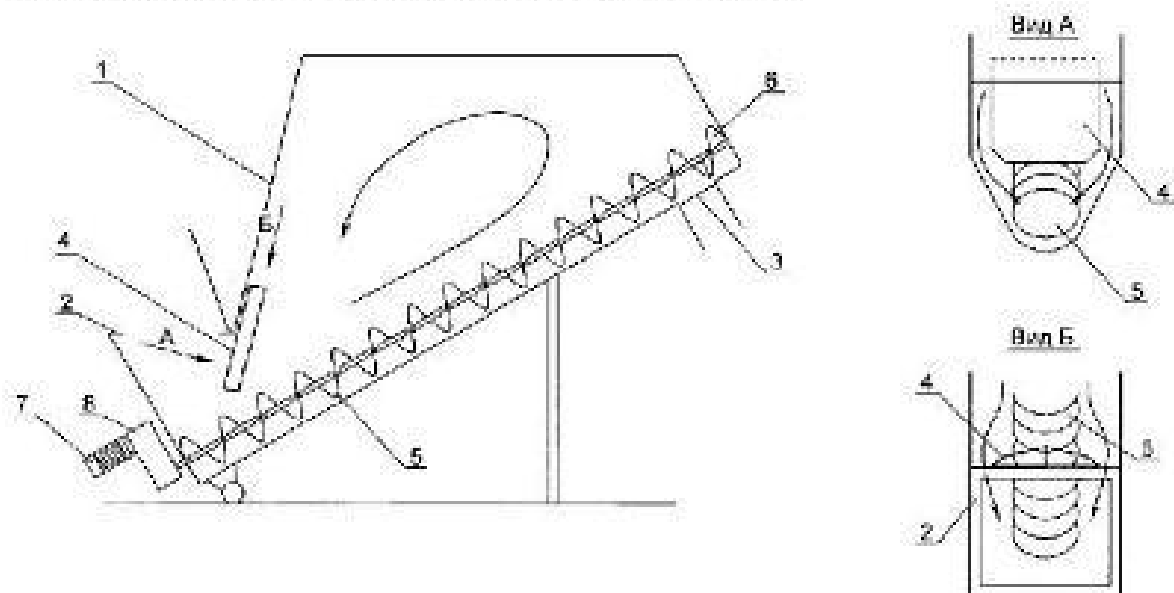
Смеситель кормов (Патент РФ № 2328950)
